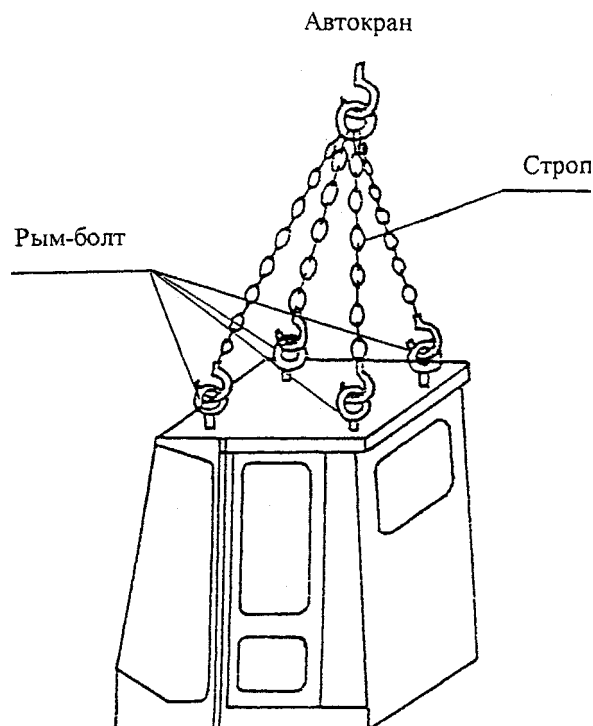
Схема строповки корпуса кабины У7810.7-9
